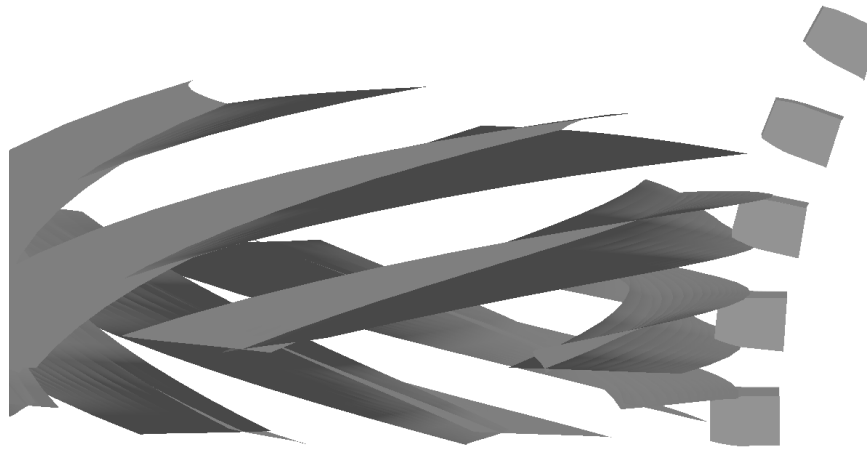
OpenGL промальовка в Eclipse SDK зачеплення гіперболоїдного шліфувального кола й циліндричного зубчастого колеса
